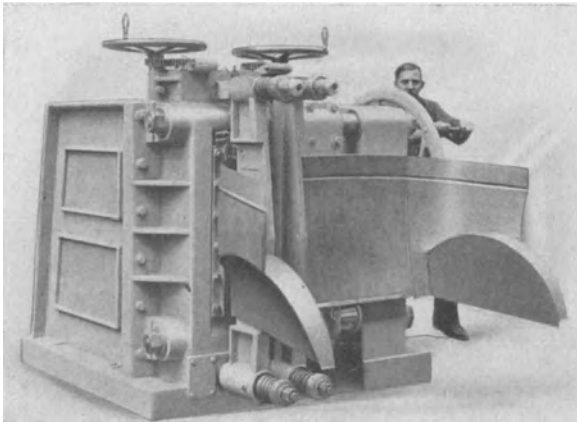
Abbrennschweißen von Karosserierückwandnähten.
